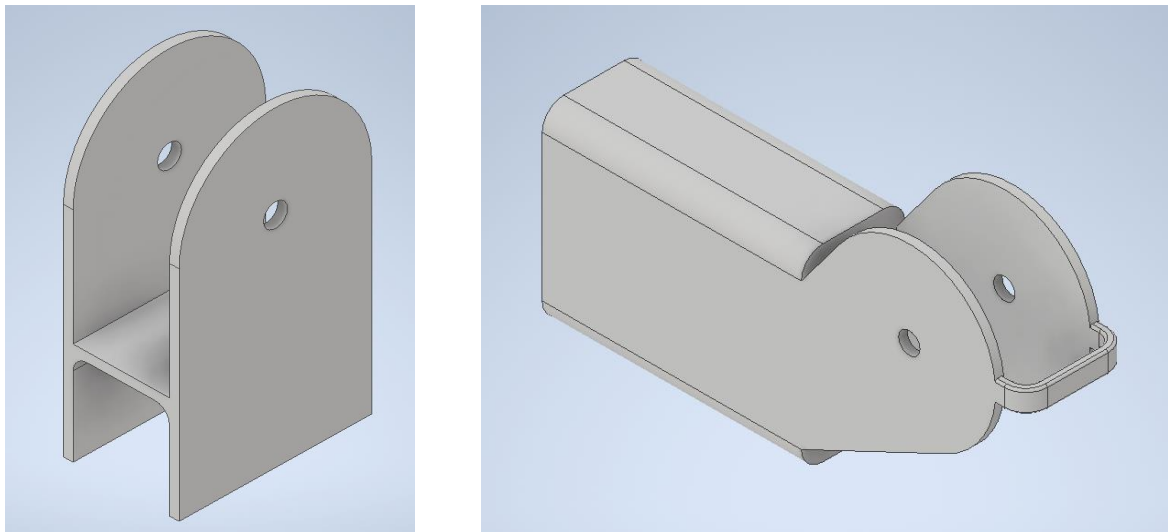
Soportes de la roldana: codo (izquierda) y extremo (derecha).
